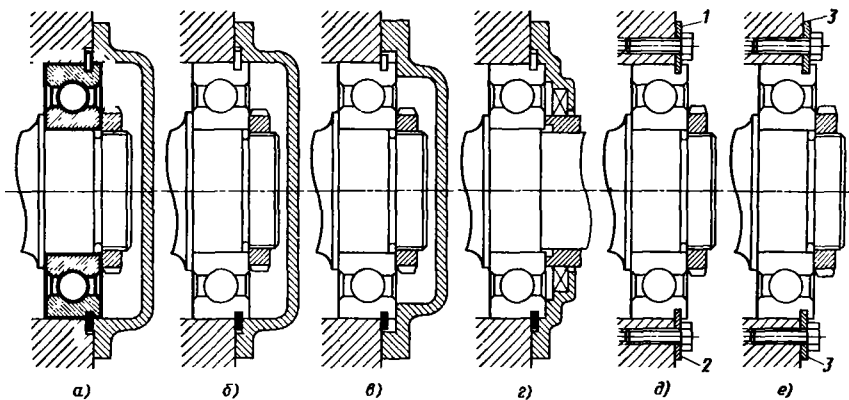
Крепление подшипников с помощью разрезных пружинных колец
